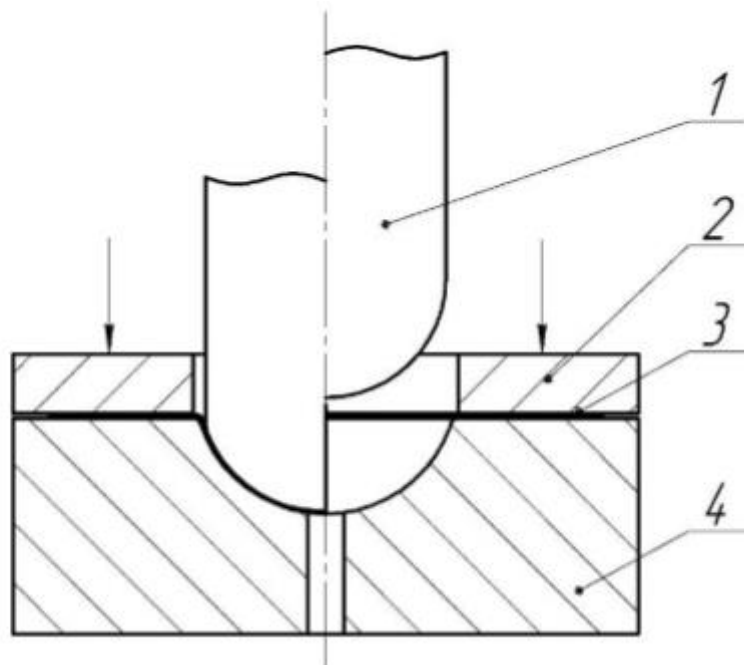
Схема листового витягування в жорсткому штампі: 1 – пуансон; 2 – притискач; 3 – заготівля; 4 – матриця
